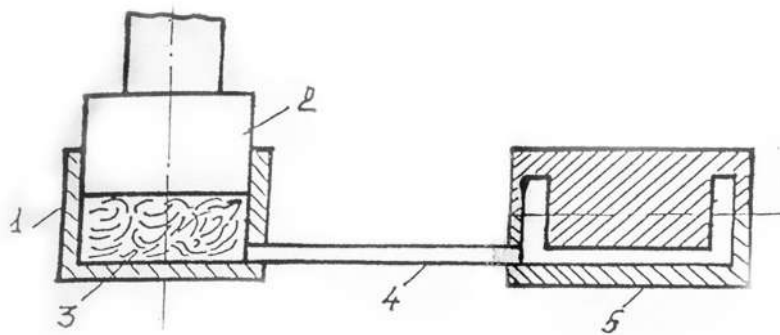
Схема изготовления пластмассовых изделий пресс-литьем.
